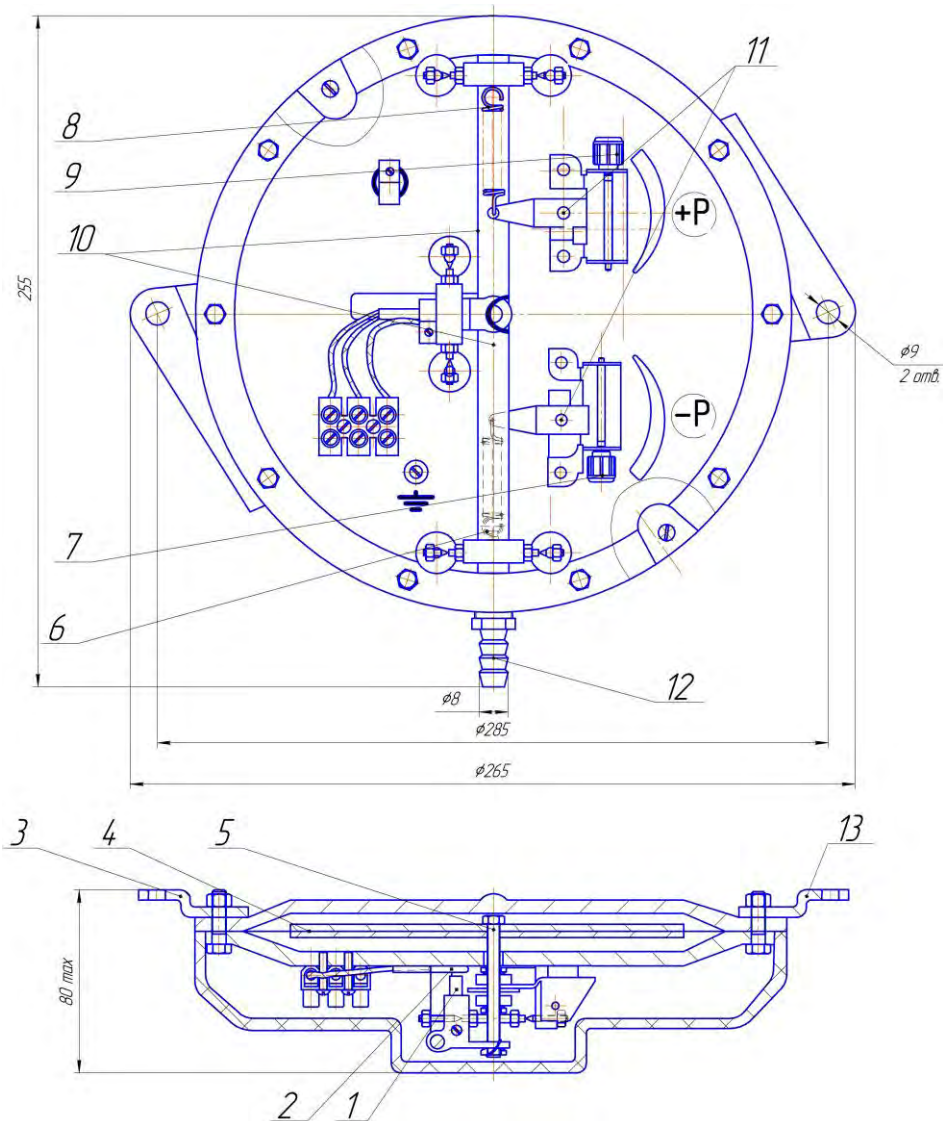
Габаритные и присоединительные размеры датчика-реле напора и тяги ДЕМ107
